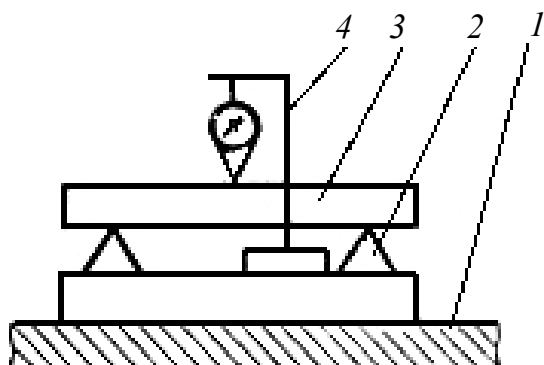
Схема проверки станка на плоскостность рабочей поверхности стола:
